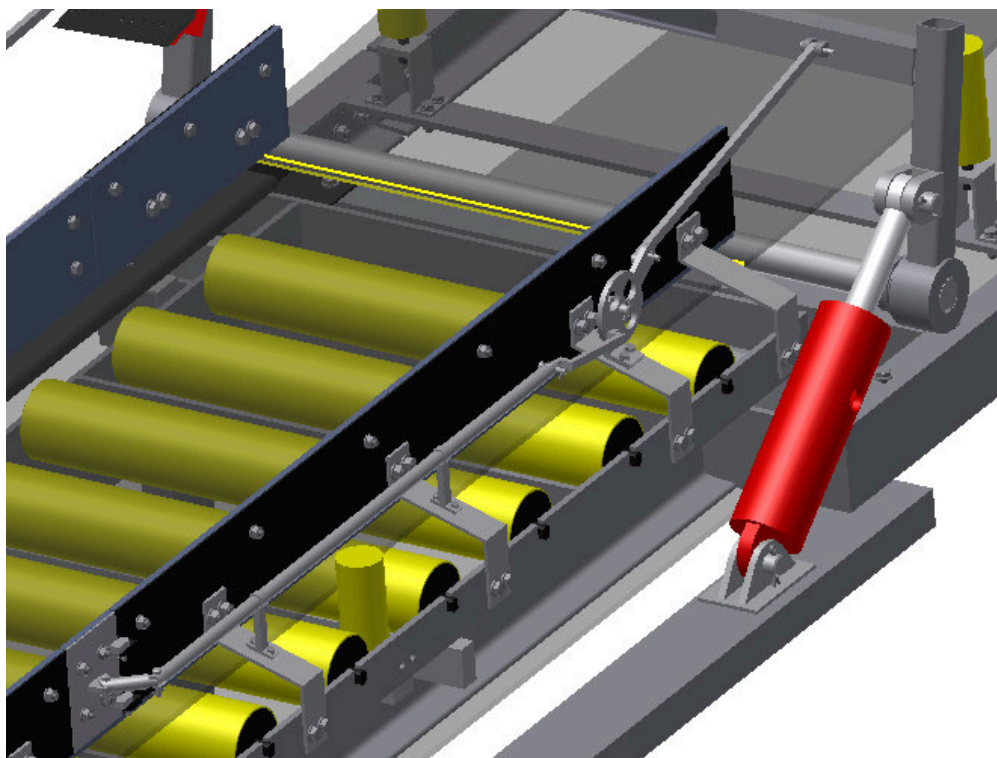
Schéma polohy mechanismu při otevřené bočnici na straně hydraulického pístu – pohled z boku
